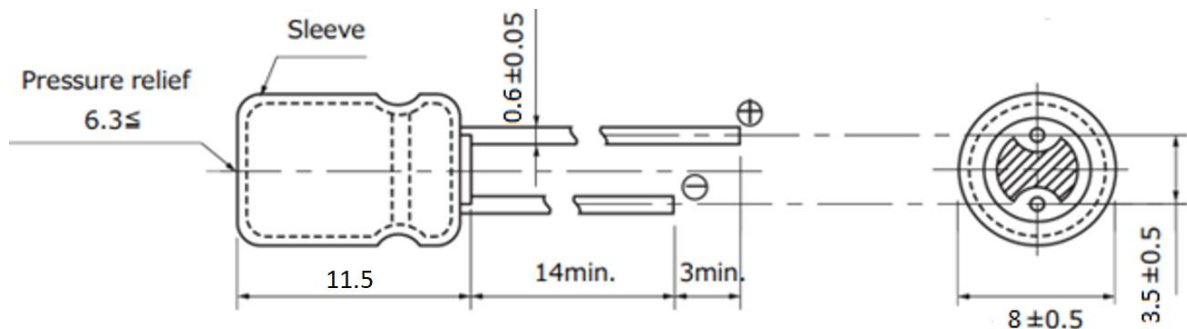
Габаритні розміри конденсатора EEU-FR1H4R7
